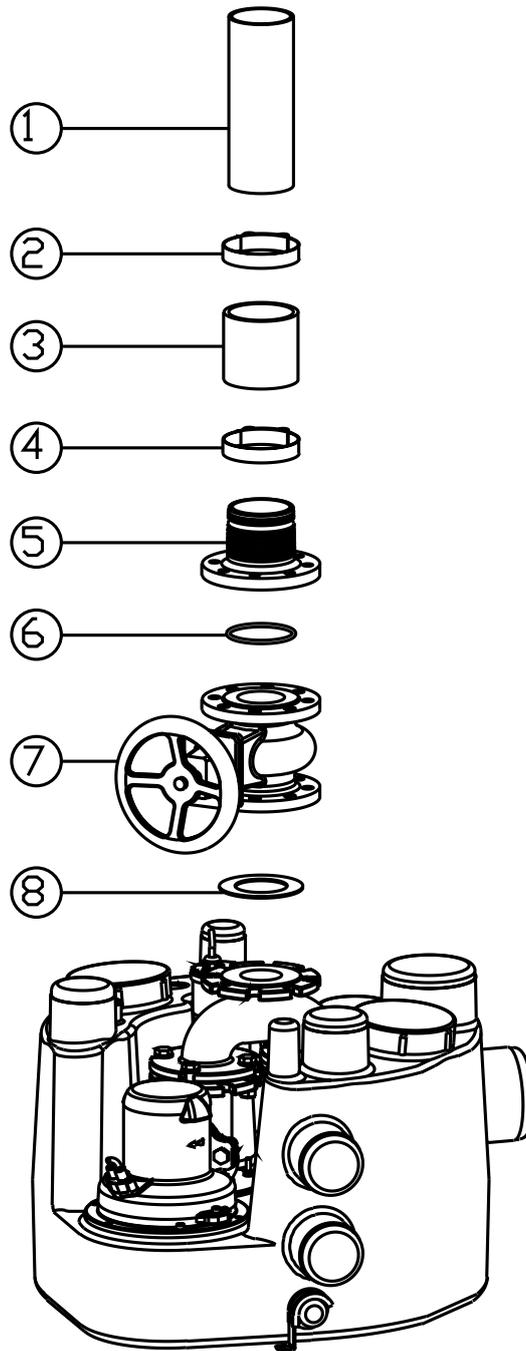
Installation du robinet d'arrêt et du manchon à bride
